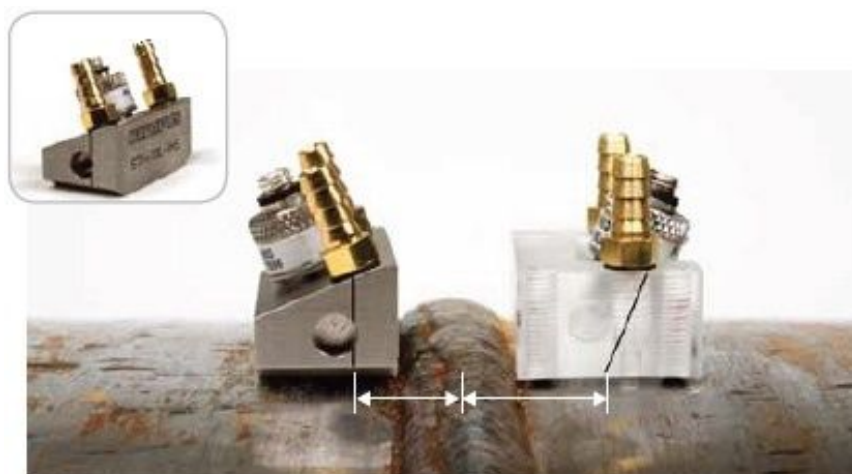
Расположение призм из нержавеющей стали ручного ультразвукового дефектоскопа Olympus CHAIN относительно сварного шва
